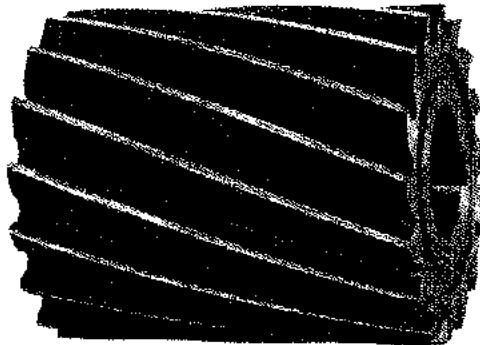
Fresa cilíndrica con dientes en espiral (Brown & Sharpe Mfg. Co.)
